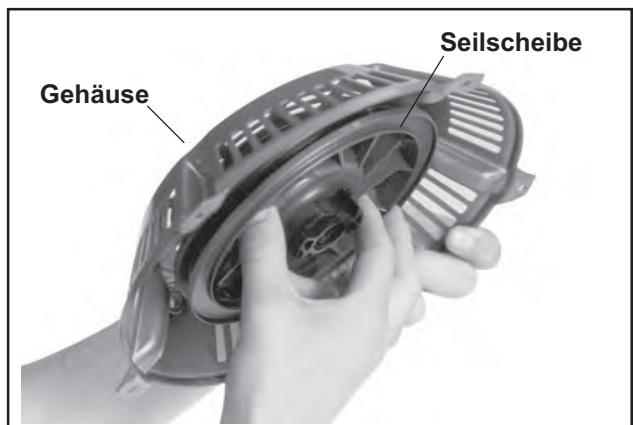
Entfernung der Seilscheibe aus dem Gehäuse.
